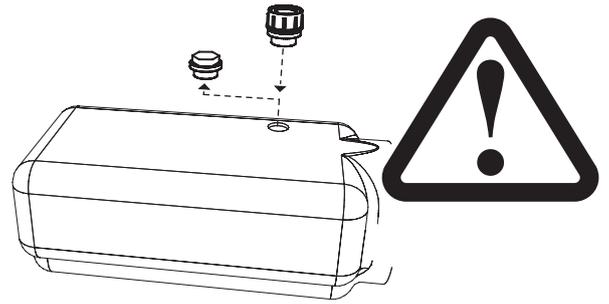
Remplacement du bouchon de transport par un bouchon de remplissage
